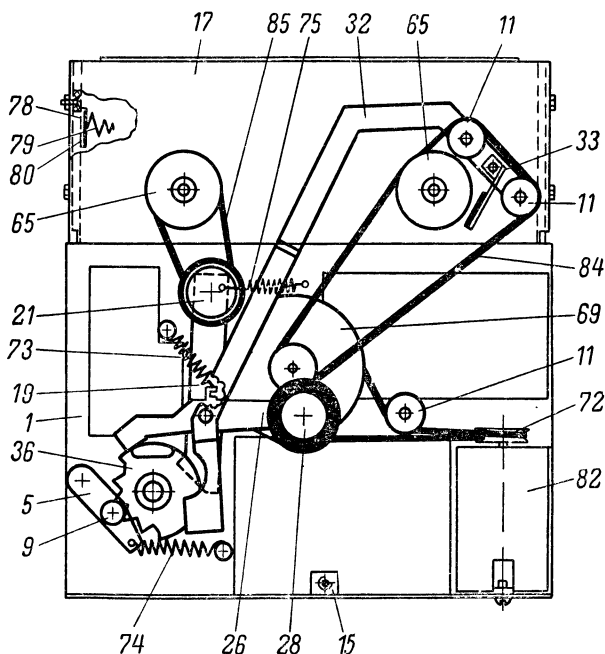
Сборочный чертеж лентопротяжного механизма магнитофона.
